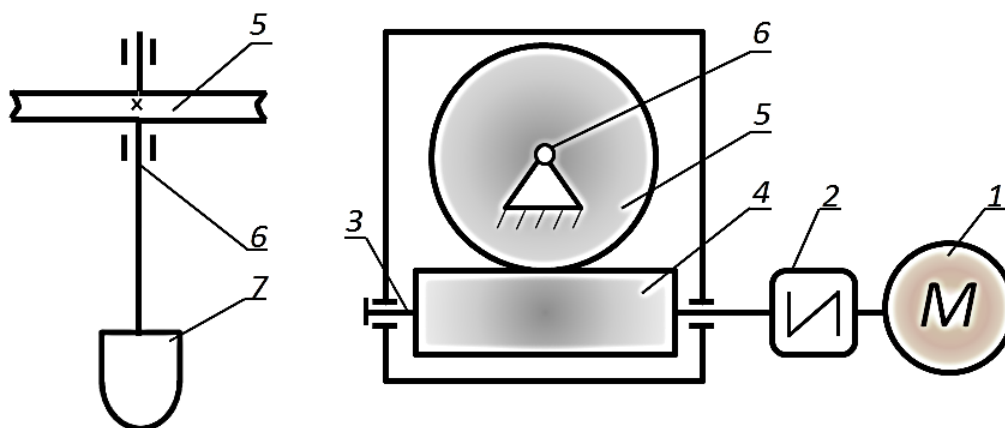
Схема привода якорной мешалки котла 28-2А:
